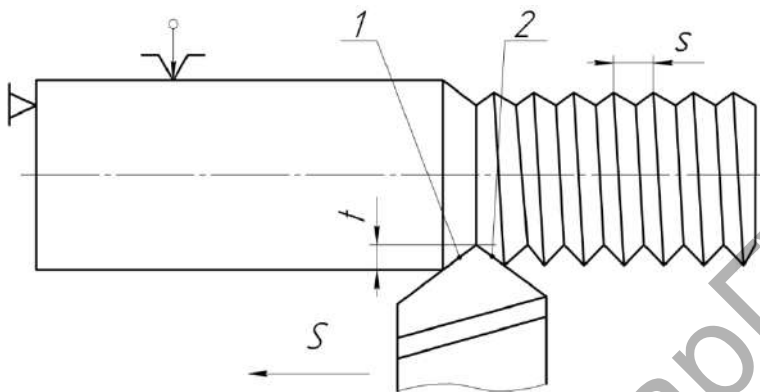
Схема контакта режущих кромок резца с заготовкой
